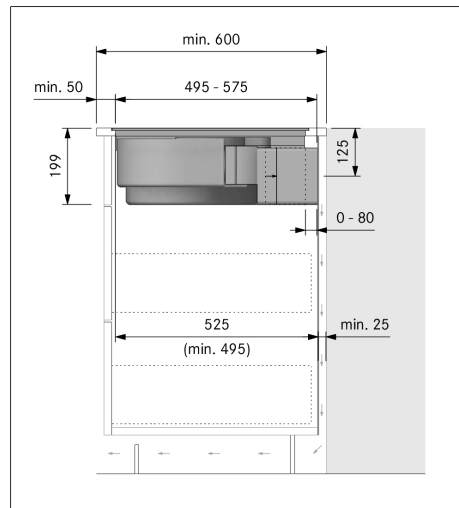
Einbaumaße bei Umluft, Montagevariante A
